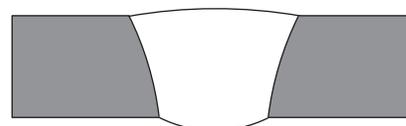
Exemple de soudure incorrecte n° 6
